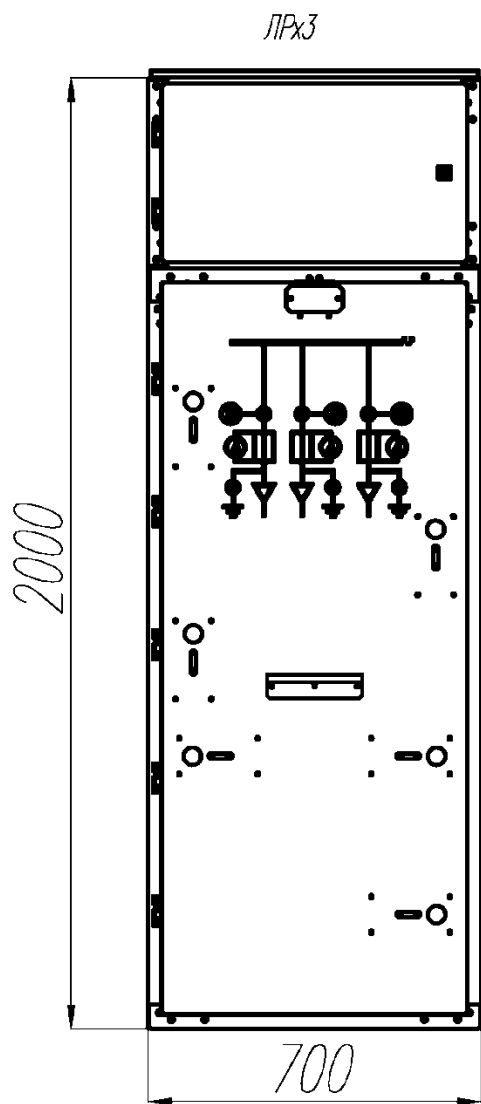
Габаритные и присоединительные размеры РУОШ-600 (ЛРхЗ и АРхЗ)
